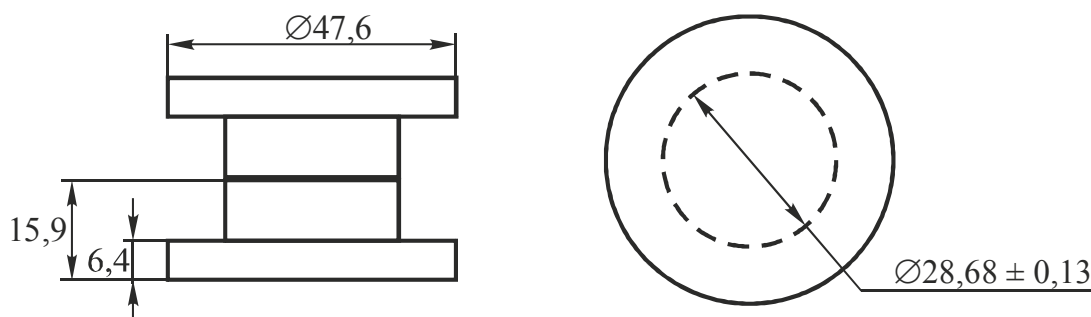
Форма и размеры (в мм) образца согласно стандарту ASTM D897–08
